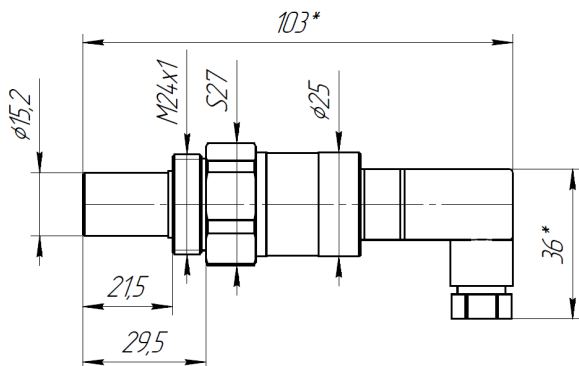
Установочные и габаритные размеры преобразователя ДВ2ТСМ-1Т-4П-В.
